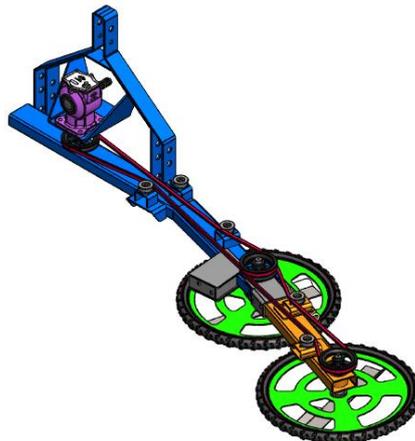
Concepção da roçadora para realizar limpeza entre plantas.
